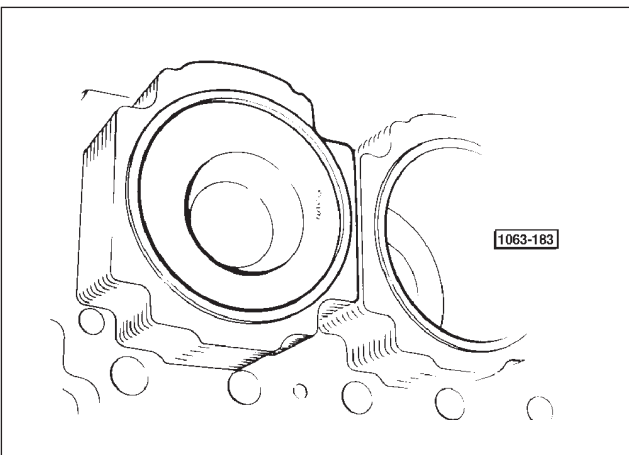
Orienter la chambre de combustion du piston du côté des pompes d'injection, bloquer l'ensemble piston-bielle à l'aide de l'outil 5.9030.631.4/10; par la suite retourner le bloc-moteur.
